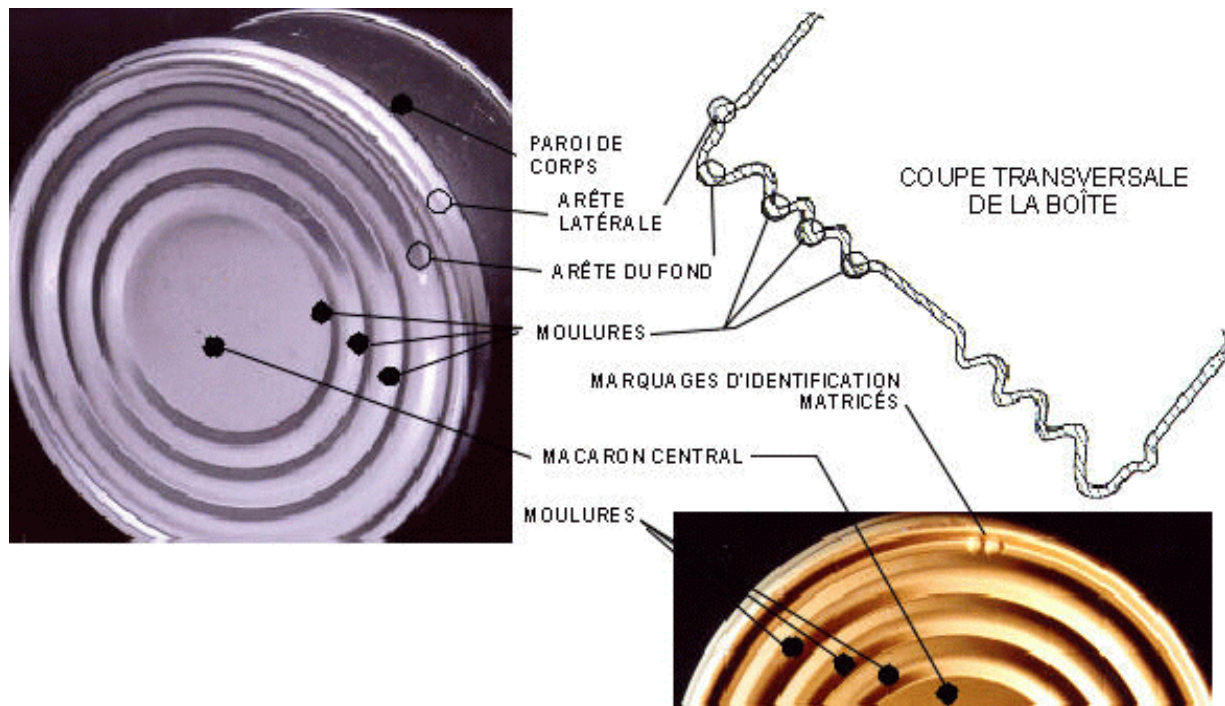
b - Boîte deux pièces - Fond intégré flexible
